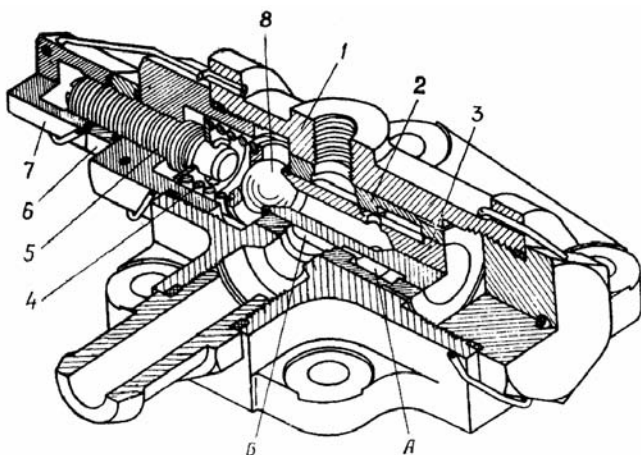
Перепускний розподільник: А, Б — проточки; 1 — корпус; 2 — втулка; 3 — перепускний клапан; 4 — пружина; 5 — гвинт регулювальний; 6 — контргайка; 7 — ковпачок; 8 — кулька.
